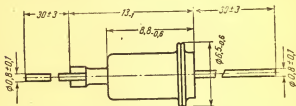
Габаритный чертеж диодов 2C156A, 2C168A.
